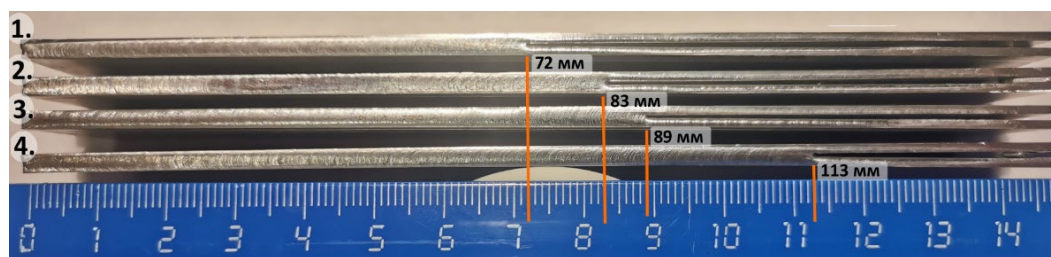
Сварка образцов с различными типами разверток. 1 – сварка без развертки, 2 – сварка с синусоидальной разверткой, 3 – развертка меандр, 4 – развертка треугольник
